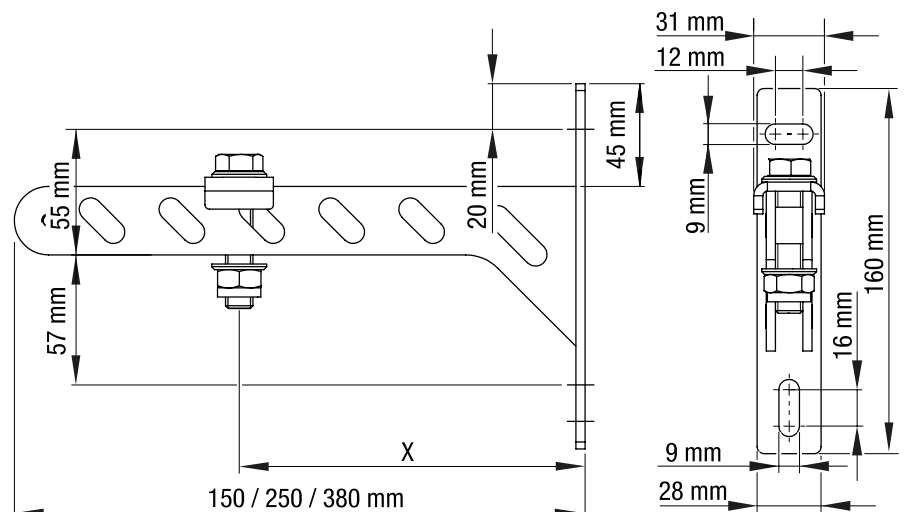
Wandarm für Abhängungen – Einbaumaße
